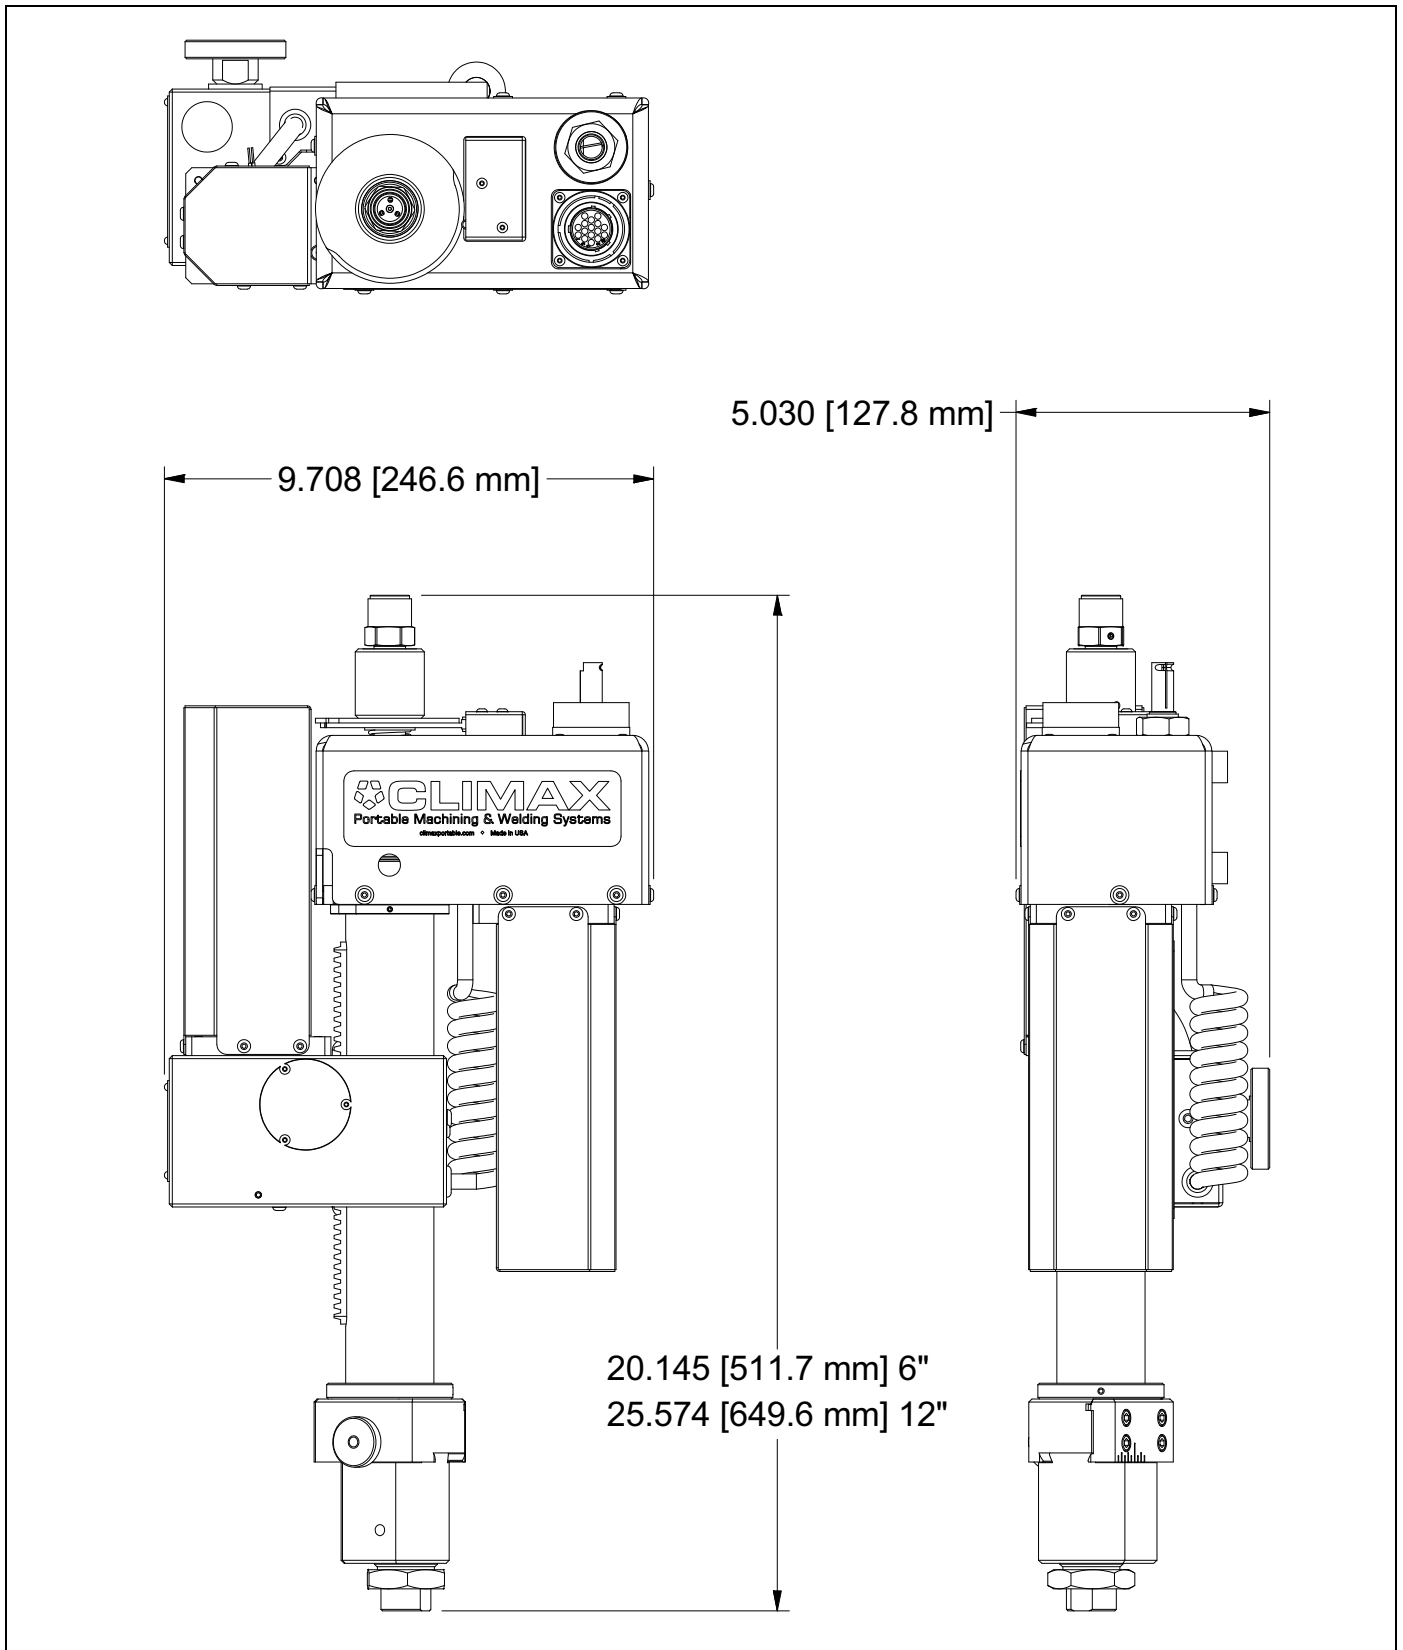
DIMENSIONES DE BW3000 (N/P 103159)
